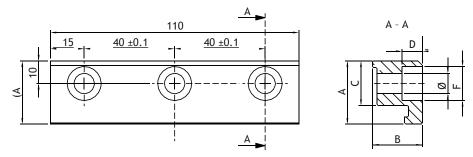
Disegno dimensionato di una staffa di fissaggio corta
